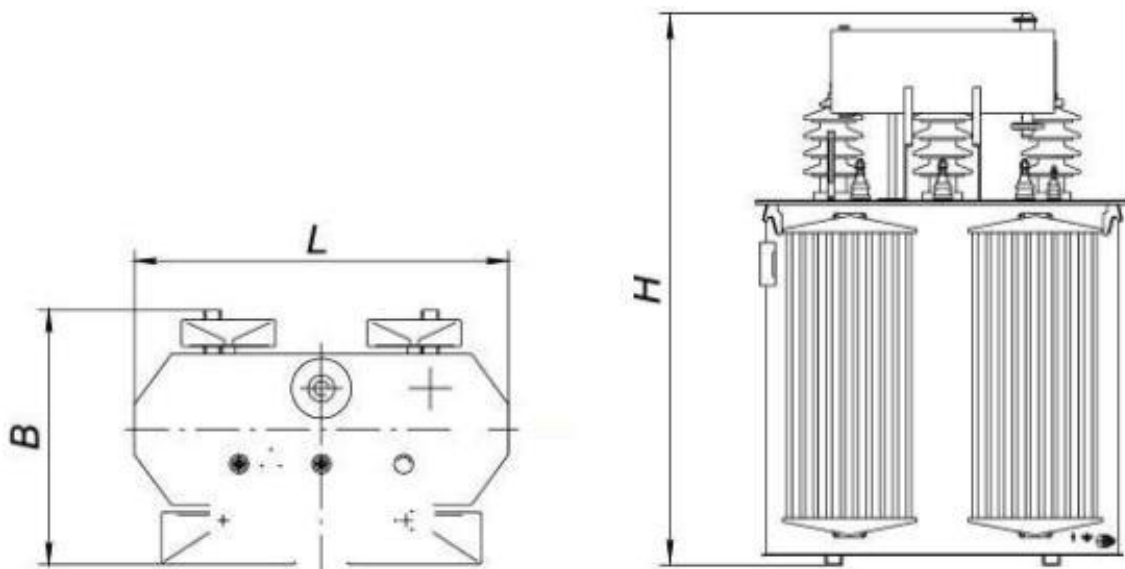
Габаритный рисунок трансформатора ТМ - 4000
